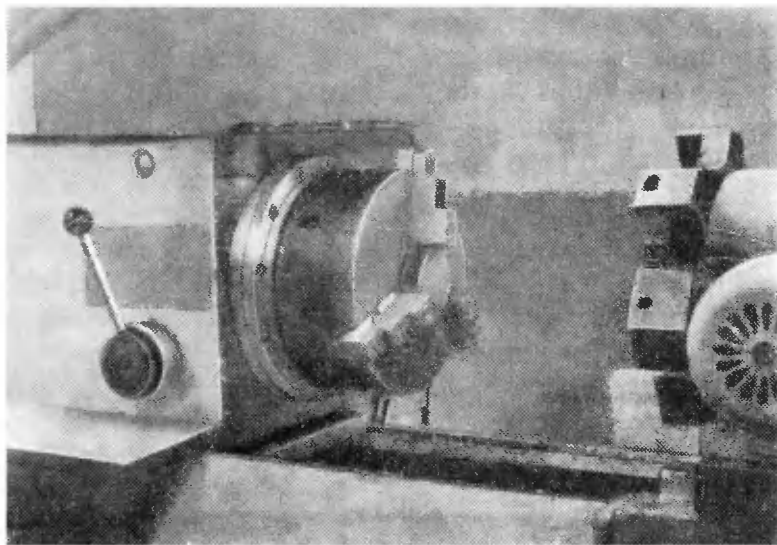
Общий вид механизированного патрона и гидроцилиндра, установленных на станке типа 16К20Ф3С5.
